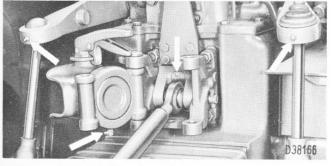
Bielles de relevage, lame de ressort, chape d'attelage
